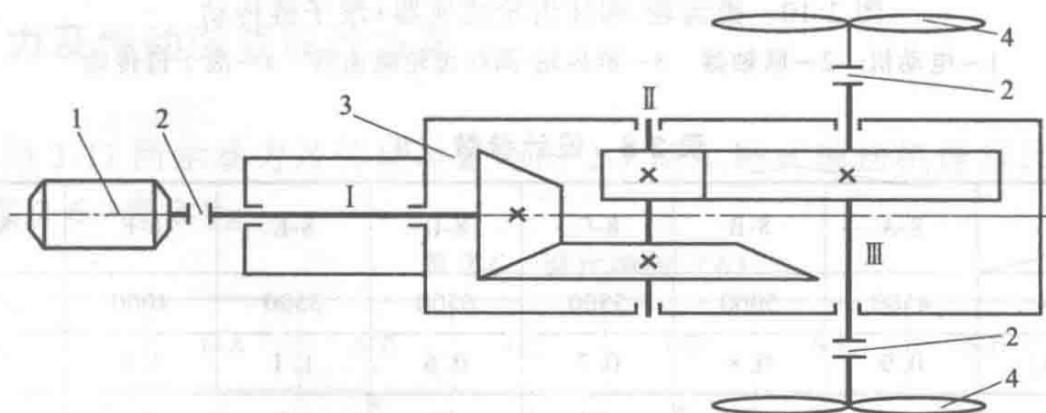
锥齿轮-圆柱齿轮减速器+搅拌器
